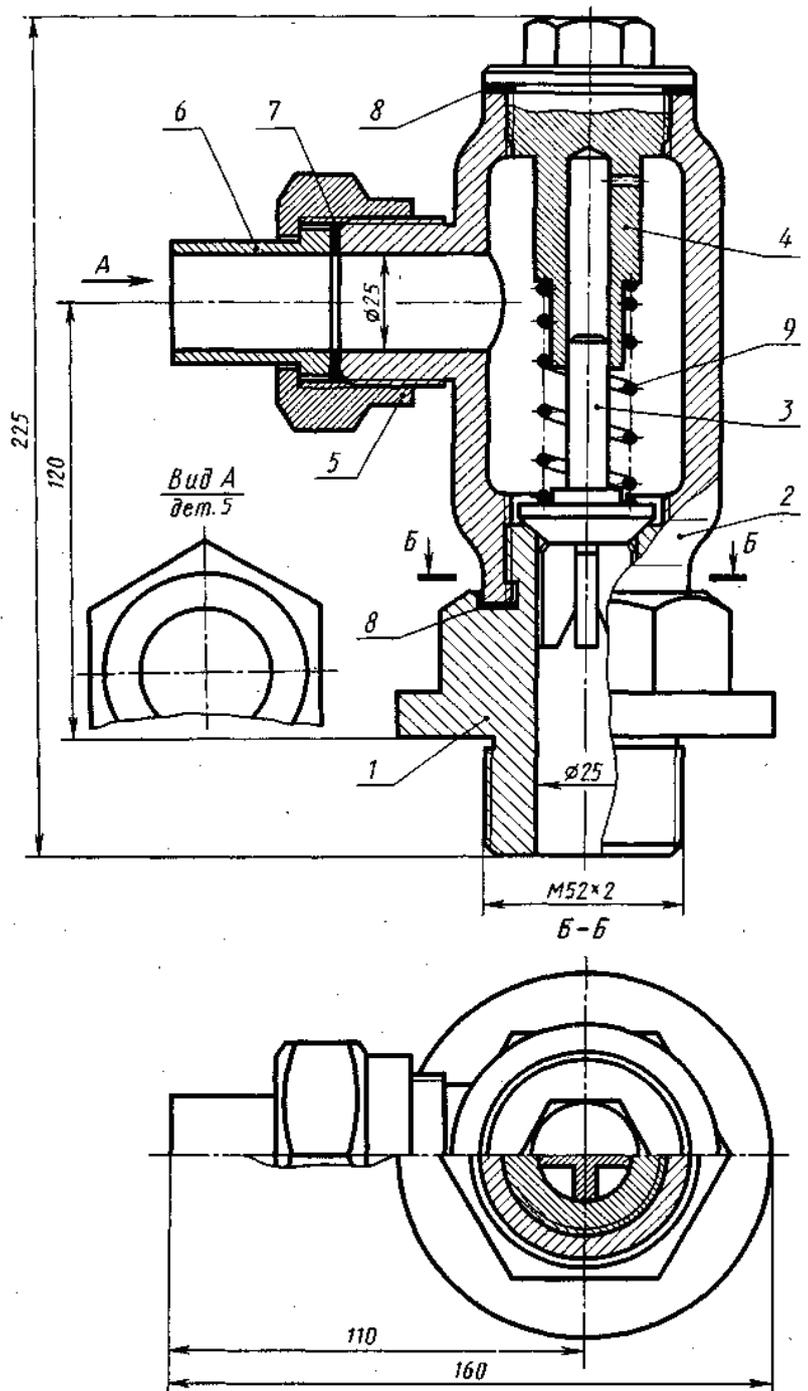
Сборочный чертеж сборочной единицы «Клапан обратный»
